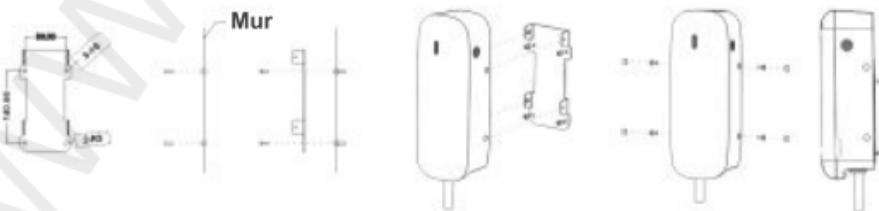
Schéma d'installation murale du chargeur de Type C
